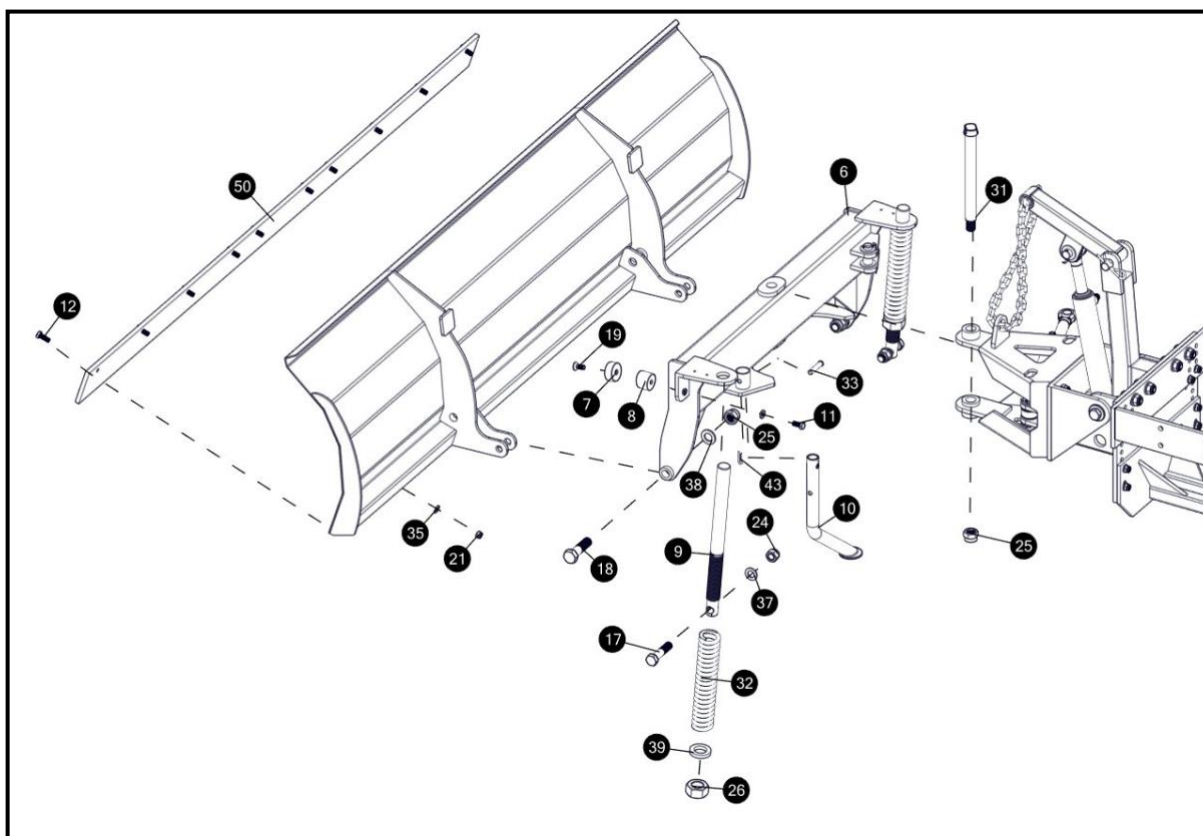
Установка отвала с поворотным механизмом на трактор
